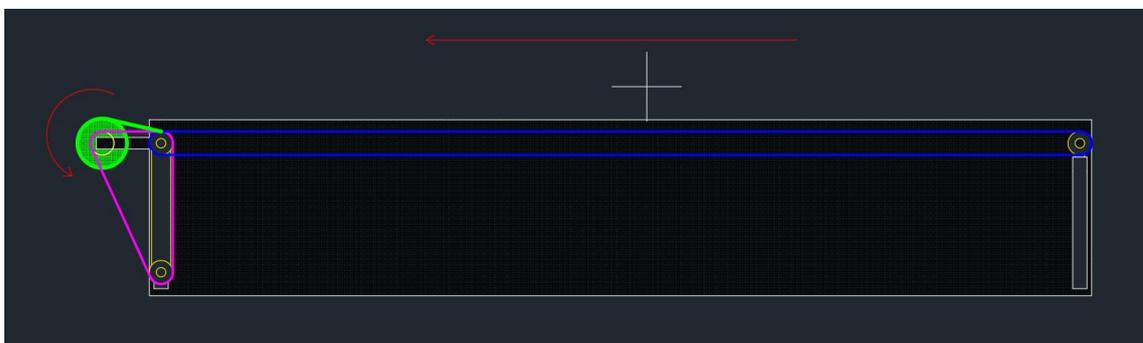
Sistema eje-cable con lona enrollada y cilindros bajados.
